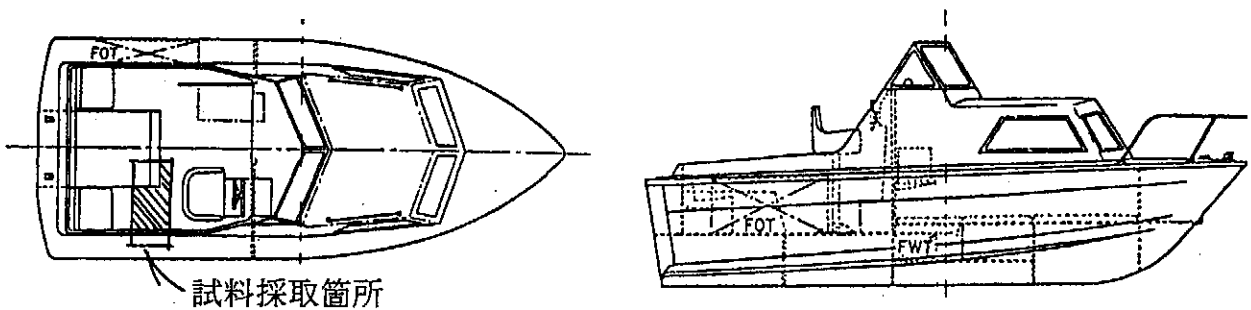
6 m 艇の一般配置図<sup>3)</sup>
